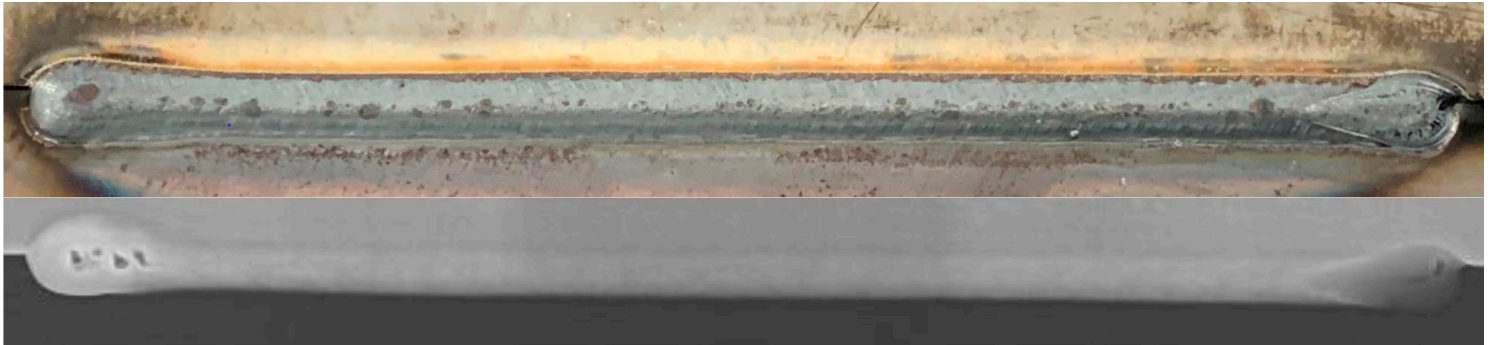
Imagen de superficie y radiografía digital de soldaduras que demuestran una porosidad interna del 1% o menos. Alambre ER70S-3 soldado en MPH 660GI 60G/60G.
